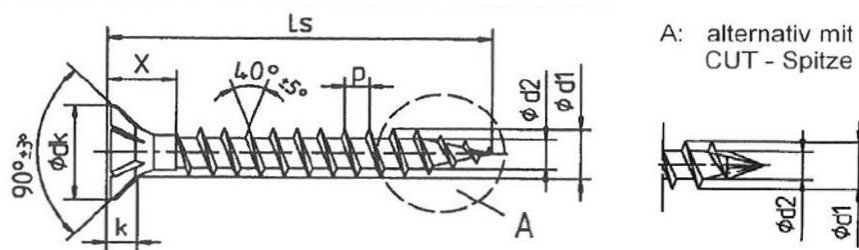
Skizze der Holzbauschraube „SPAX-S“ [38]
